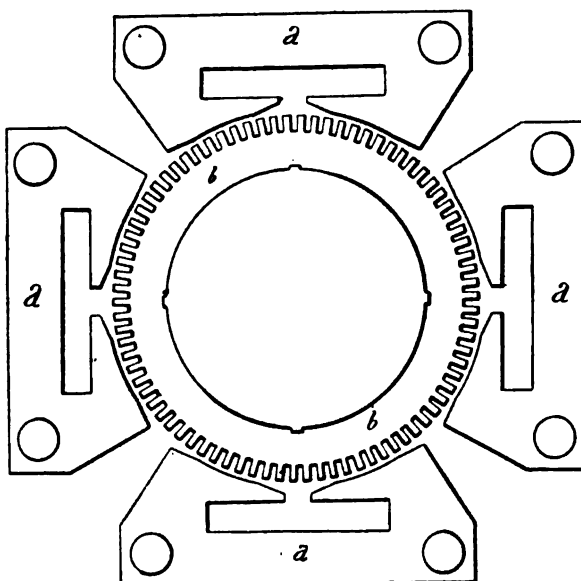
Lames de tôle des machines de 36 000 watts.
